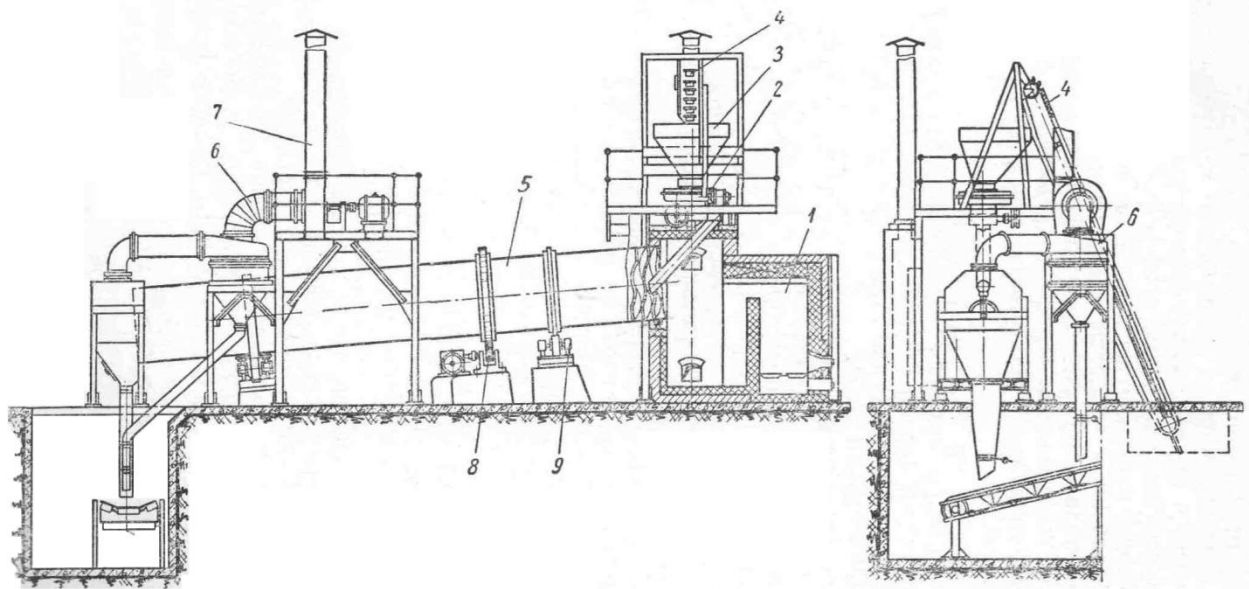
Основні частини барабанного апарату, що обертається:
